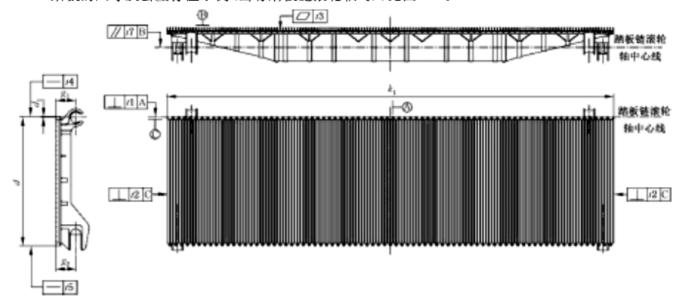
踏板(无轴)的尺寸示意图及重要尺寸公差
